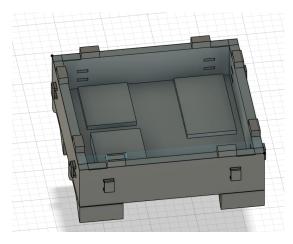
Widok rzutu bocznego na pierwsze piętro modelu.
